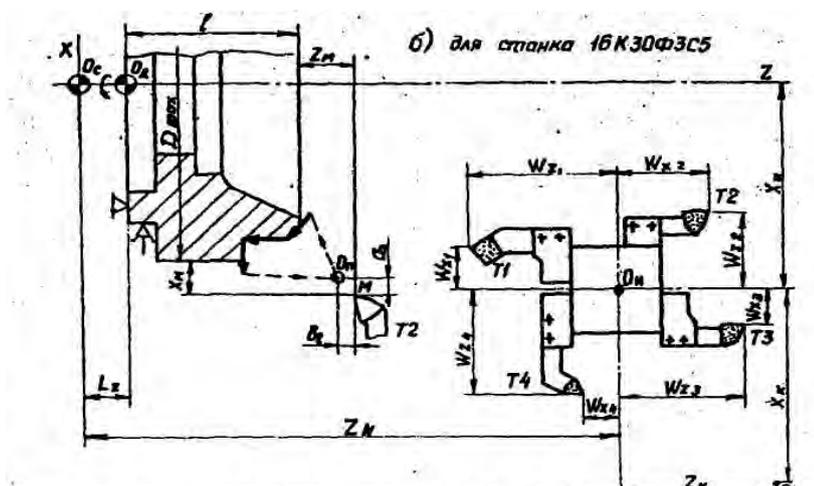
Оси координат токарного станка с ЧПУ
